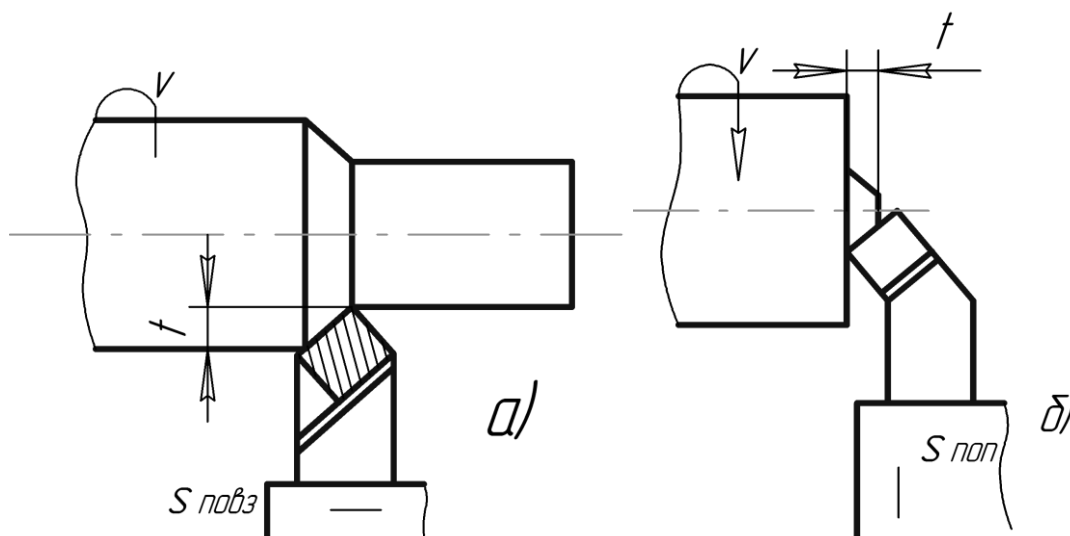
Схеми робочих рухів при токарній обробці:
